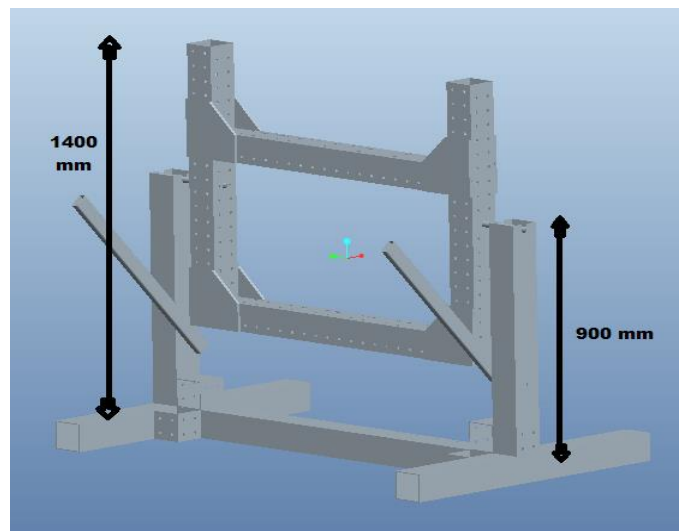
Cuerpo principal que conforma la base para el potro de soldadura propio
